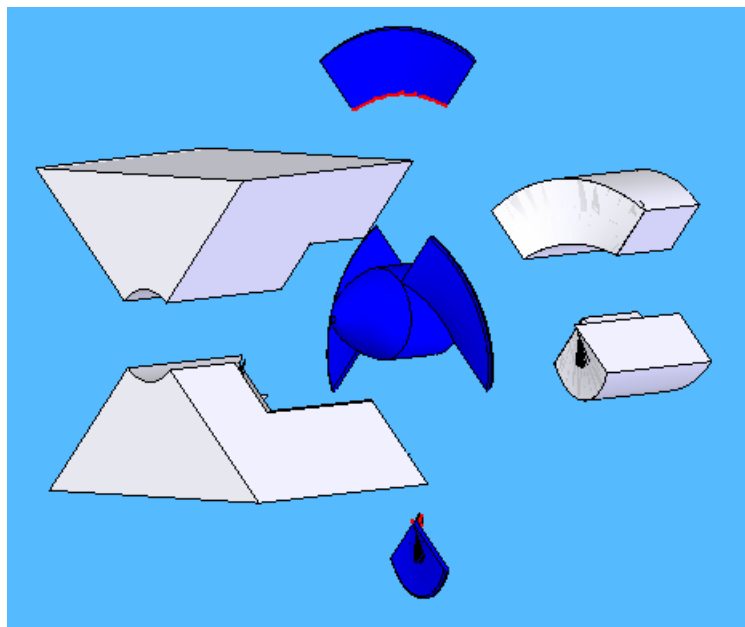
Esquema del montaje previo a la soldadura de 2 alabes en el rotor.
